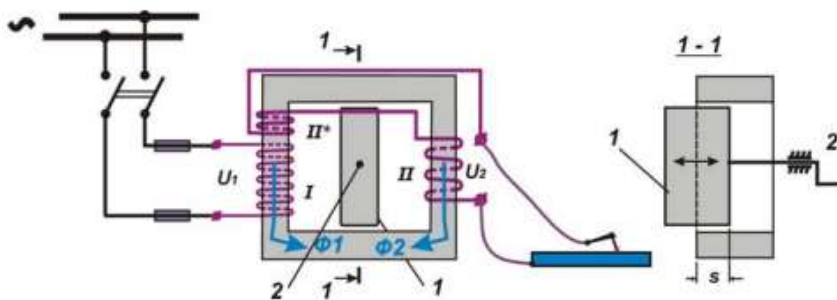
Схема сварочного трансформаторов типа СТАН I – первичная обмотка; II – вторичная обмотка основная; II*– вторичная обмотка реактивная;
